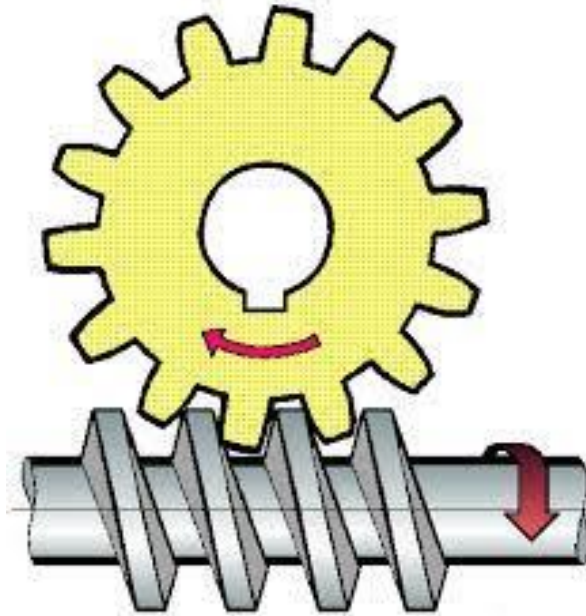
Engrenage roue dentée/Vis sans fin.
